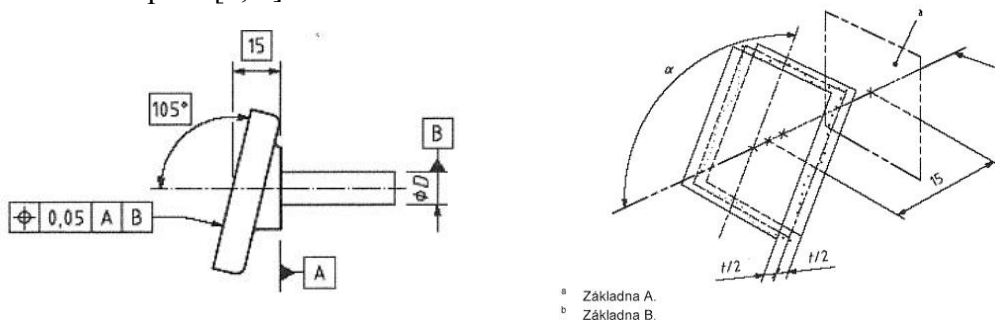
Označení a vysvětlení geometrické tolerance polohy čáry [4]
